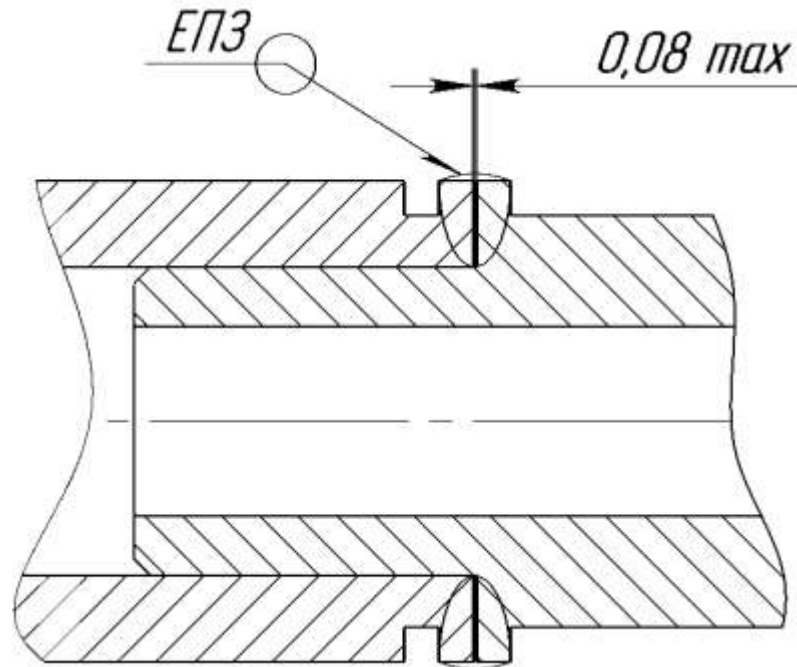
Запропонована схема зварного з'єднання з кільцевим швом
